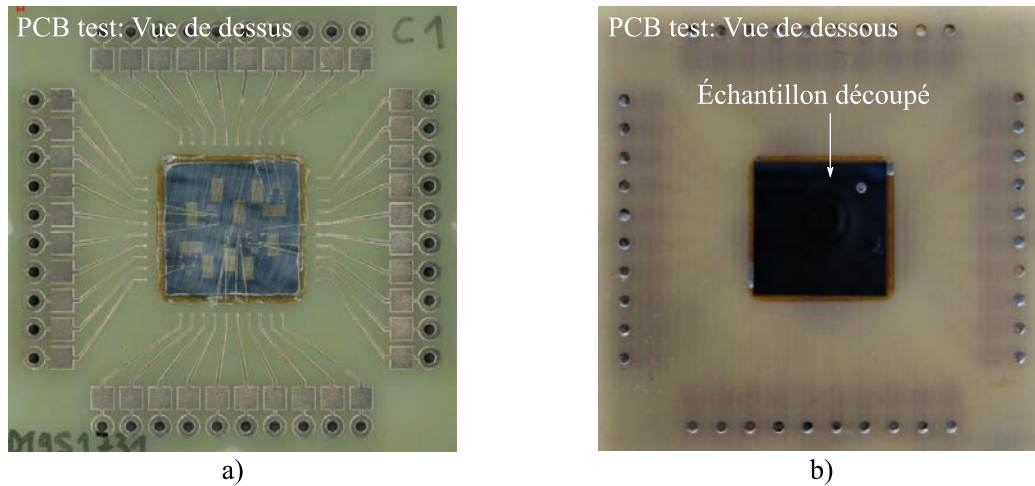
Chambre à vapeur avec élément chauffant monté sur PCB test a) en vue de dessus et b) de dessous, directement après câblage filaire.
